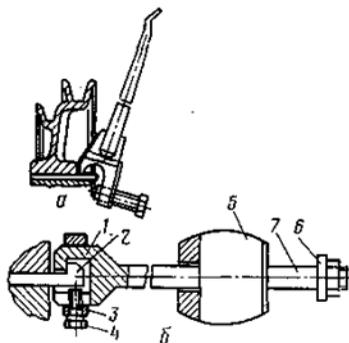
Извлечение клиновых шпонок из пазов: а – рычажным приспособлением; б – специальным съемником; 1 – головка; 2 – шпонка; 3 – кольцо; 4 – болт; 5 – груз; 6 – упор; 7 – стержень
